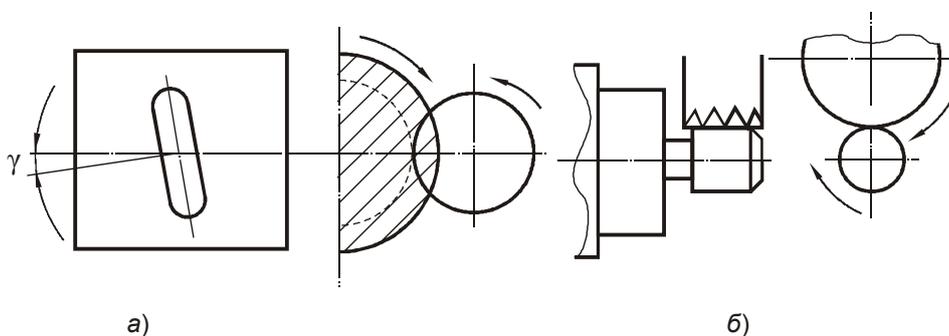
Схемы фрезерования резьбы: а – дисковой фрезой; б – групповой (гребенчатой) фрезой
